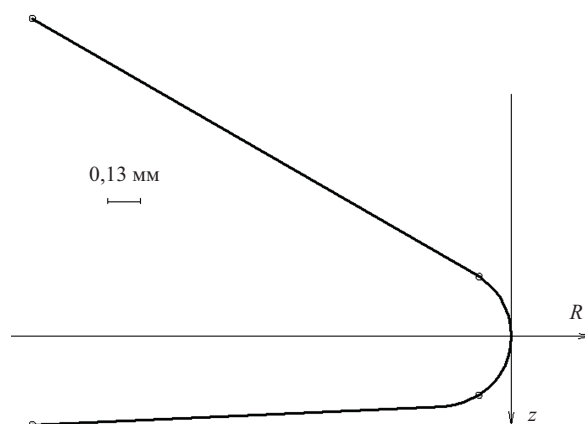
Осевое сечение инструмента для обработки резьбы S20×2
